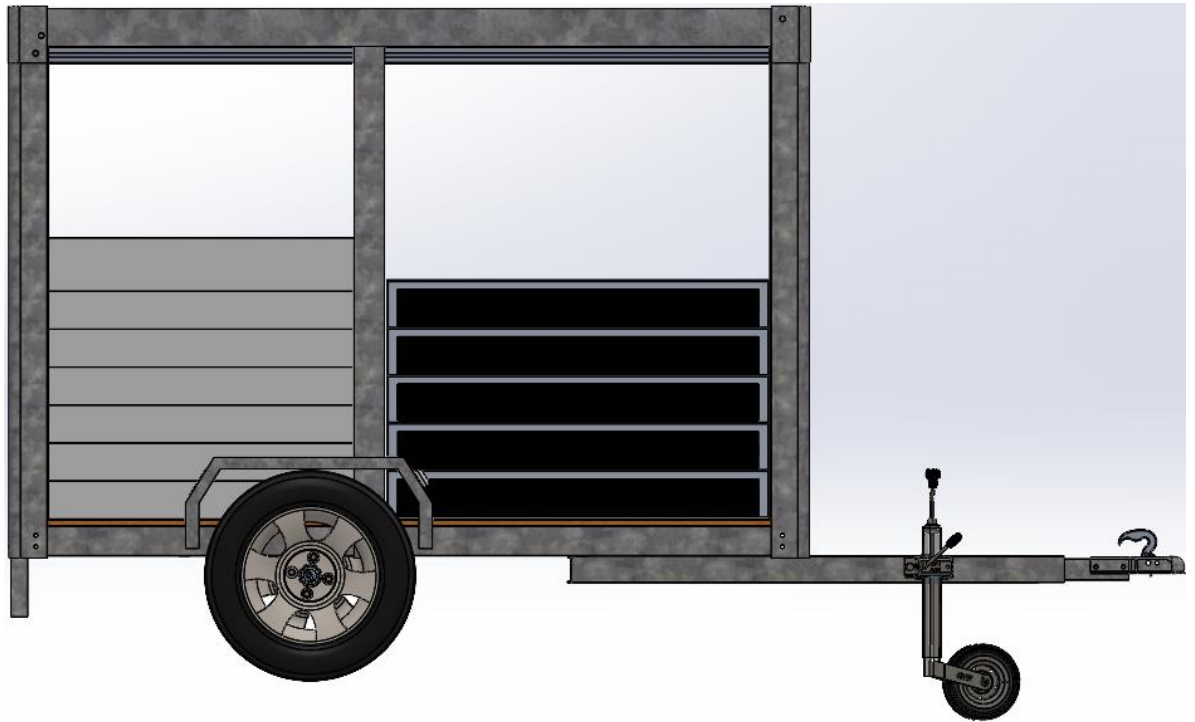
Vista perfil (Fuente: elaboración propia)
